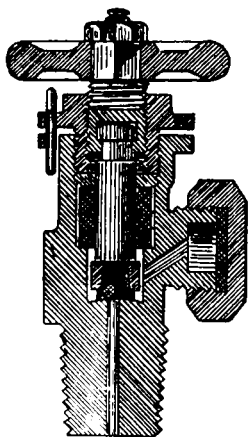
Запорный вентиль стального цилиндра для жидкой углекислоты в разрезе.
